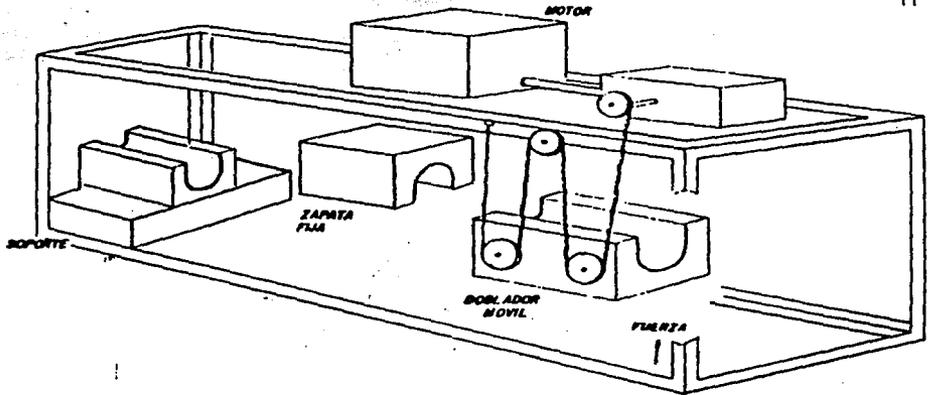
ELEMENTOS DE UNA MAQUINA DOBLADORA
